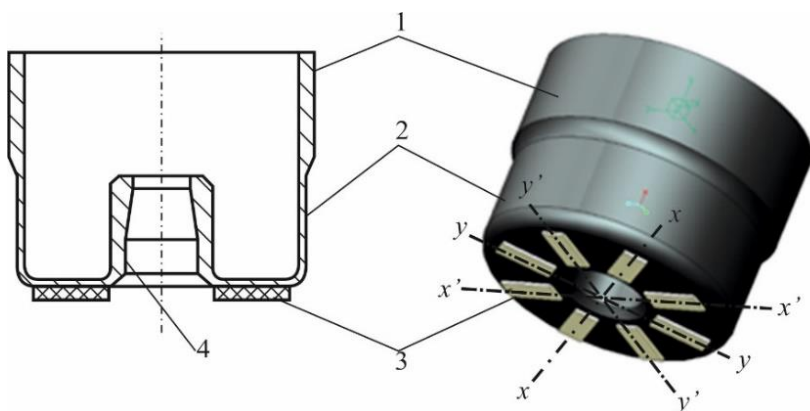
Цилиндрический резонатор: осевой разрез и общий вид
